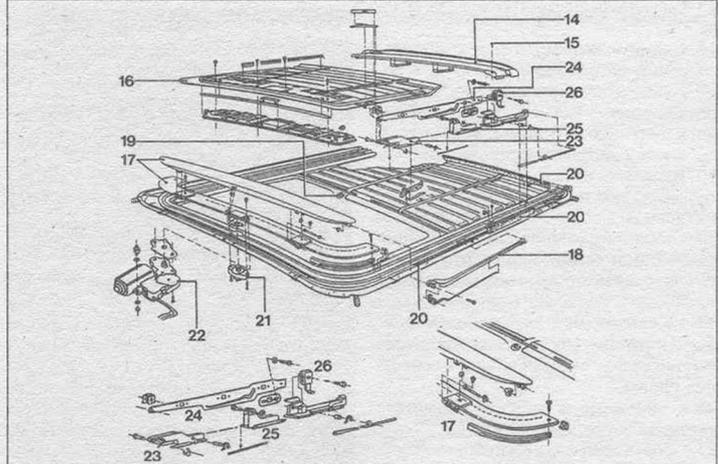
Отдельные детали люка крыши (Глава 29)
